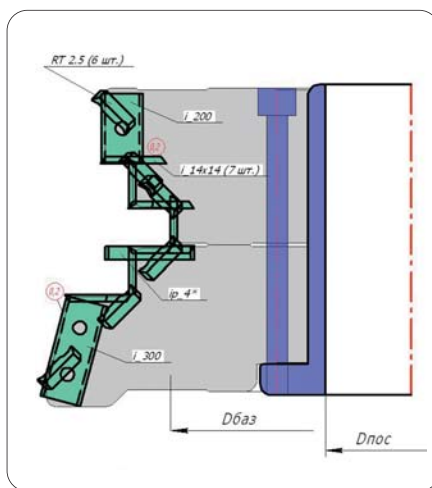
Сборная фреза «Инфлекс» с многогранными неперетачиваемыми пластинами
